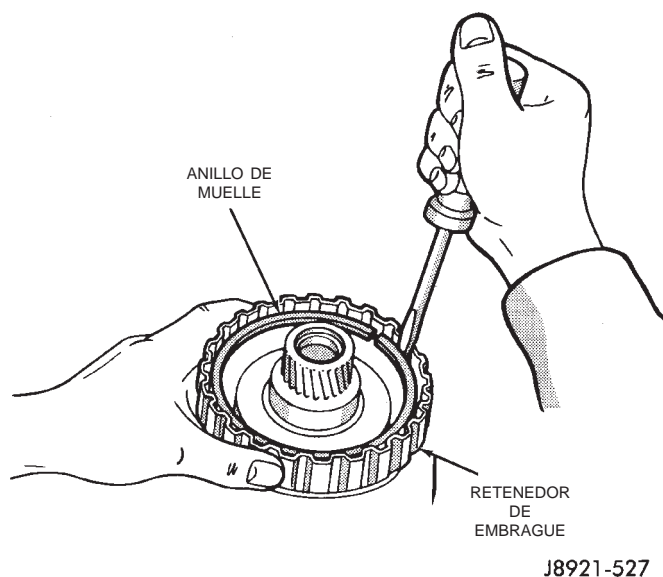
Desmontaje del anillo de muelle del conjunto de embrague
